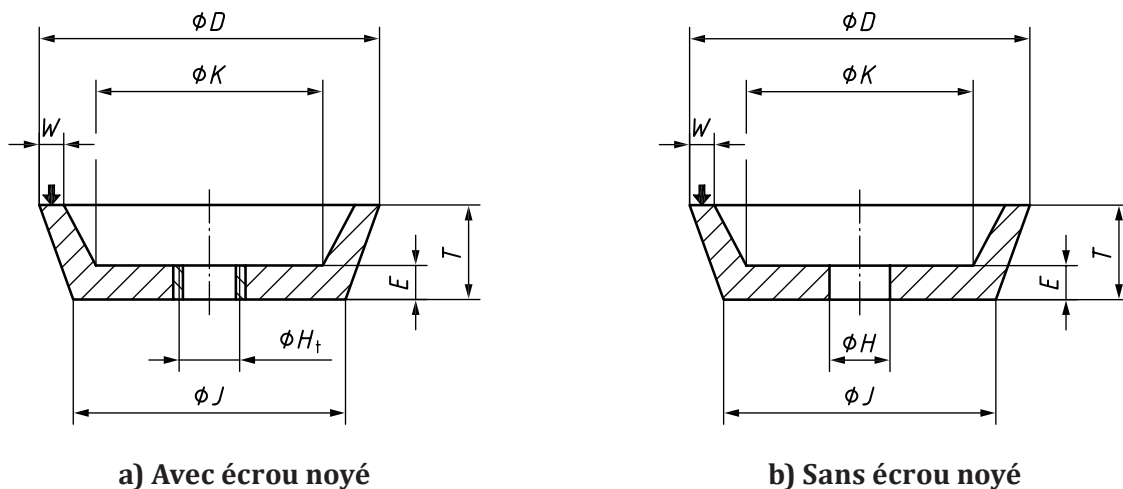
Type de forme 11 sans écrou à plaque d'ancrage ou plaque métallique au dos
